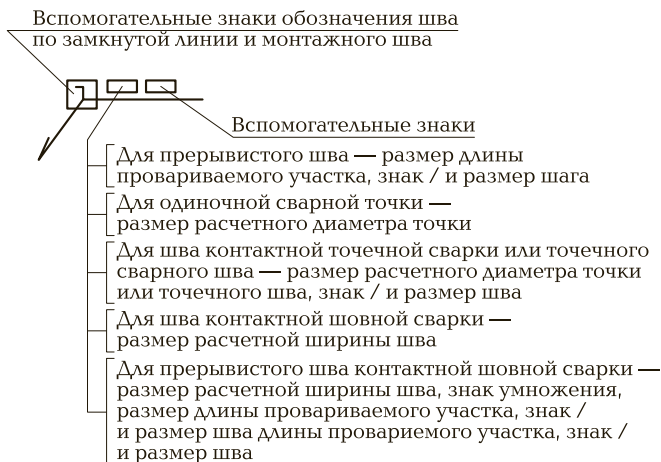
Структура условного обозначения нестандартного шва или одиночной сварной точки
